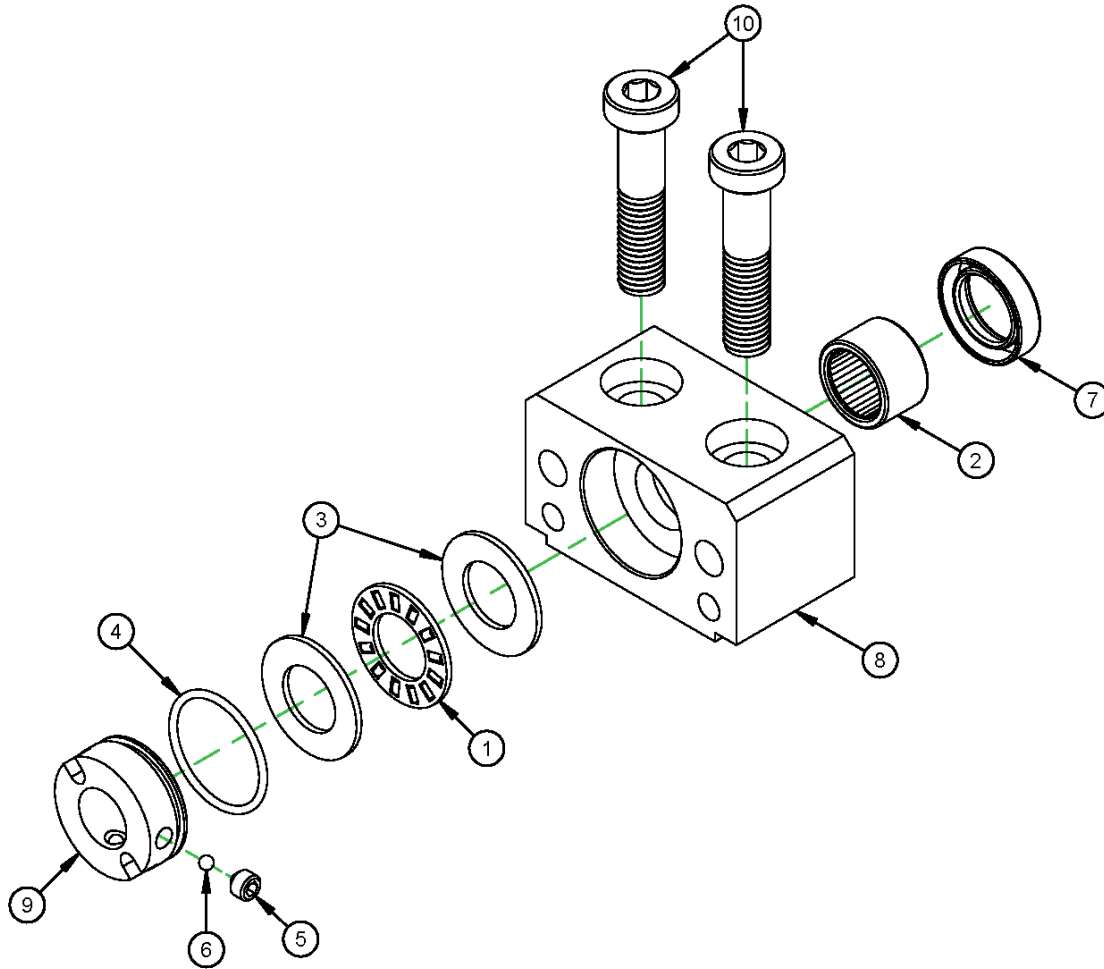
Liste de pièces ensemble coulisseau (P/N 72584)
